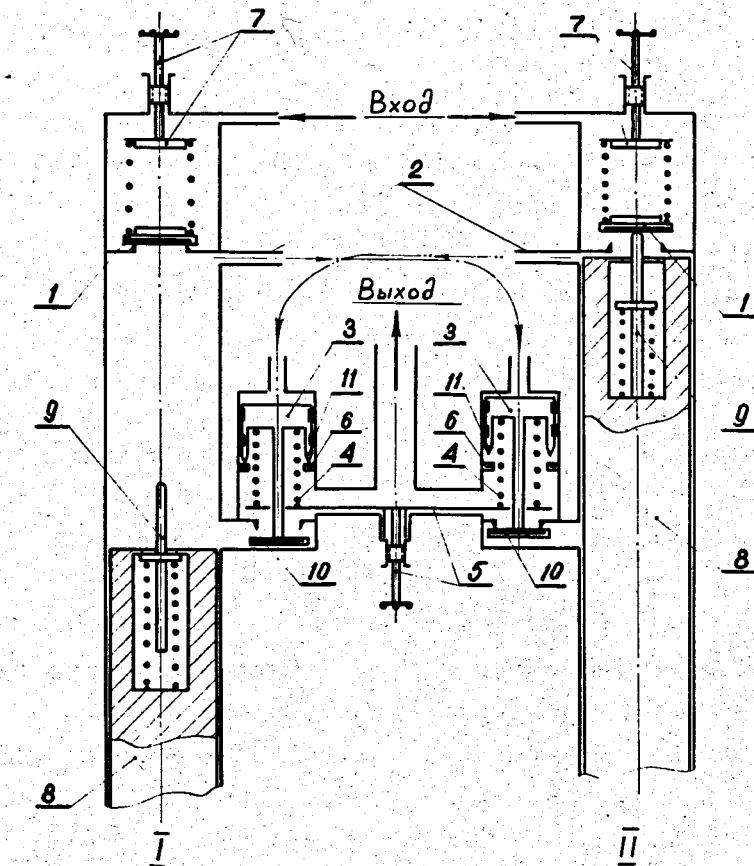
Схема детандера: 1 – клапаны впуска; 2 – газовые каналы; 3 – поршни сервоприводов; 4 – пружины; 5 – механизм регулировки отсечки выпуска; 6 – ограничители хода сервопривода; 7 – регуляторы отсечки впуска; 8 – поршни, 9 – механизм приводов впускных клапанов; 10 – клапаны выпуска, 11 – кромка поршня сервопривода.
